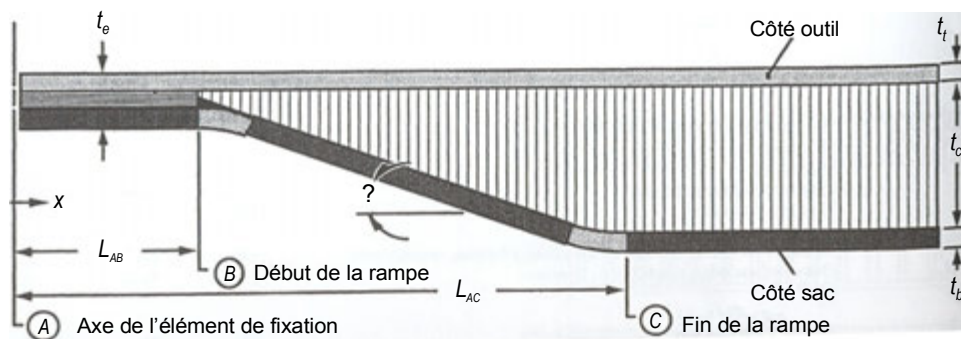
Structure sandwich avec jonction des peaux pour en permettre la fixation
